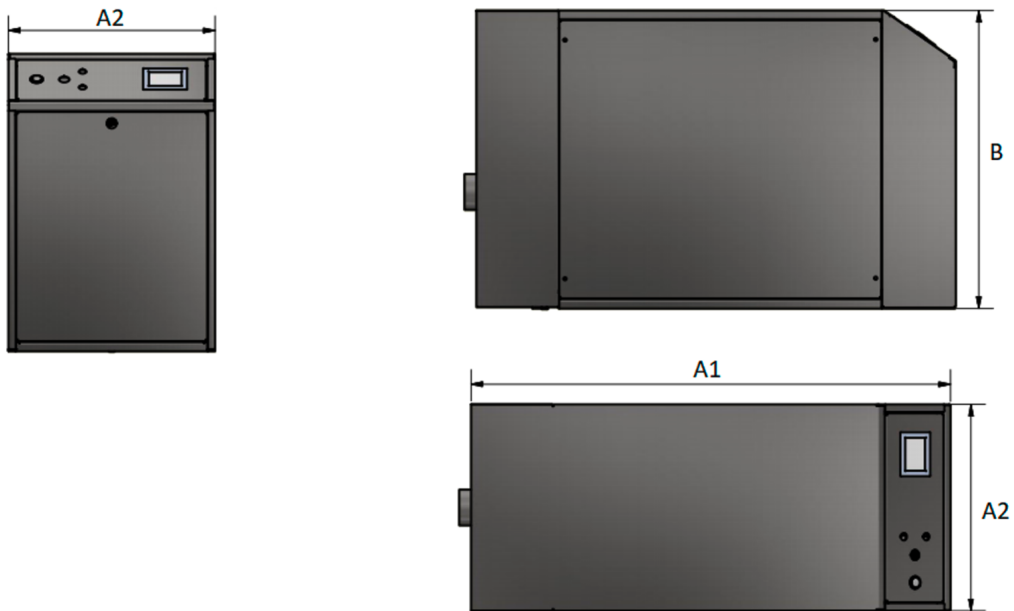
Elektrischer Dampferzeuger Typ 7121 · Abmessungen
